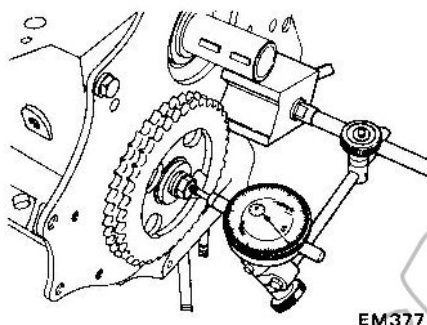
Mesure du jeu en bout de l'arbre à cames
